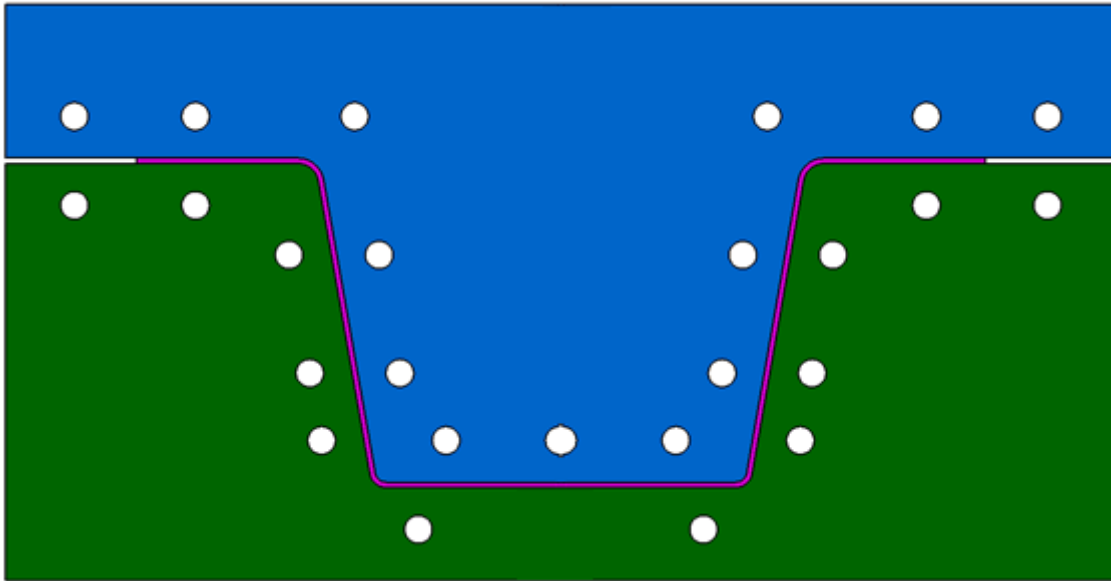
Planteamiento de la sección completa en el caso de que no exista plano de simetría
